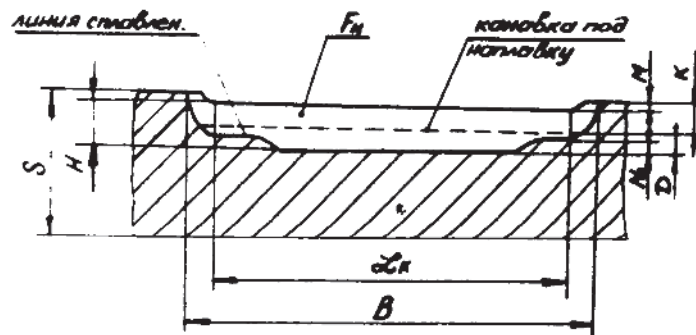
Размеры поперечного сечения наплавленного покрытия:
